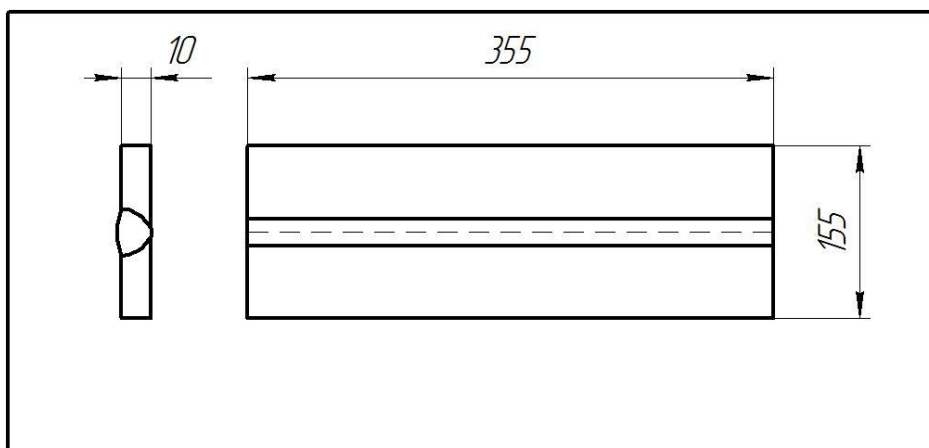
стыковой сварной образец из пластин.
